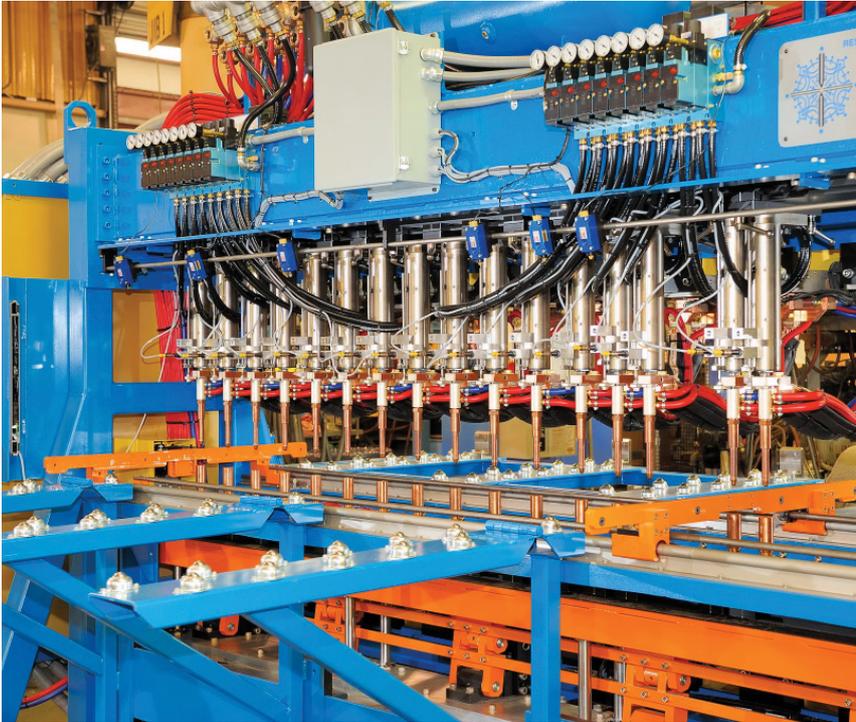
esta máquina de soldadura por puntos de 16 pistolas para puertas de presión necesita un gran volumen de refrigeración por agua.
